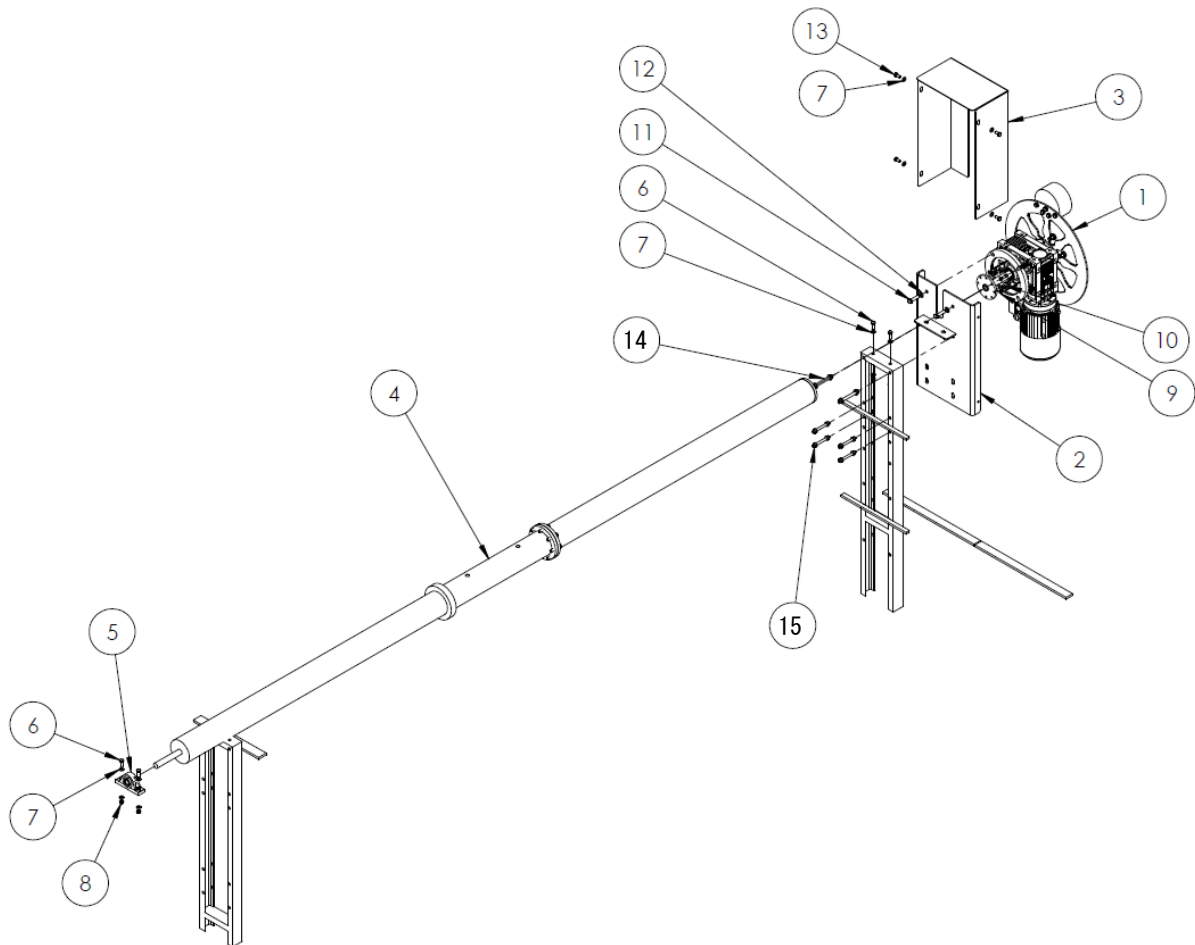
Vista explosionada del muntatge de la barra del Tarlà al carrer
